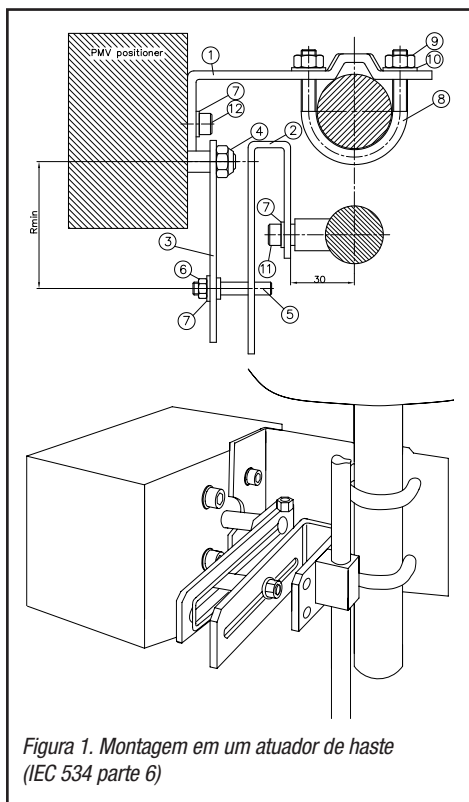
Montagem em um atuador de haste (IEC 534 parte 6)
